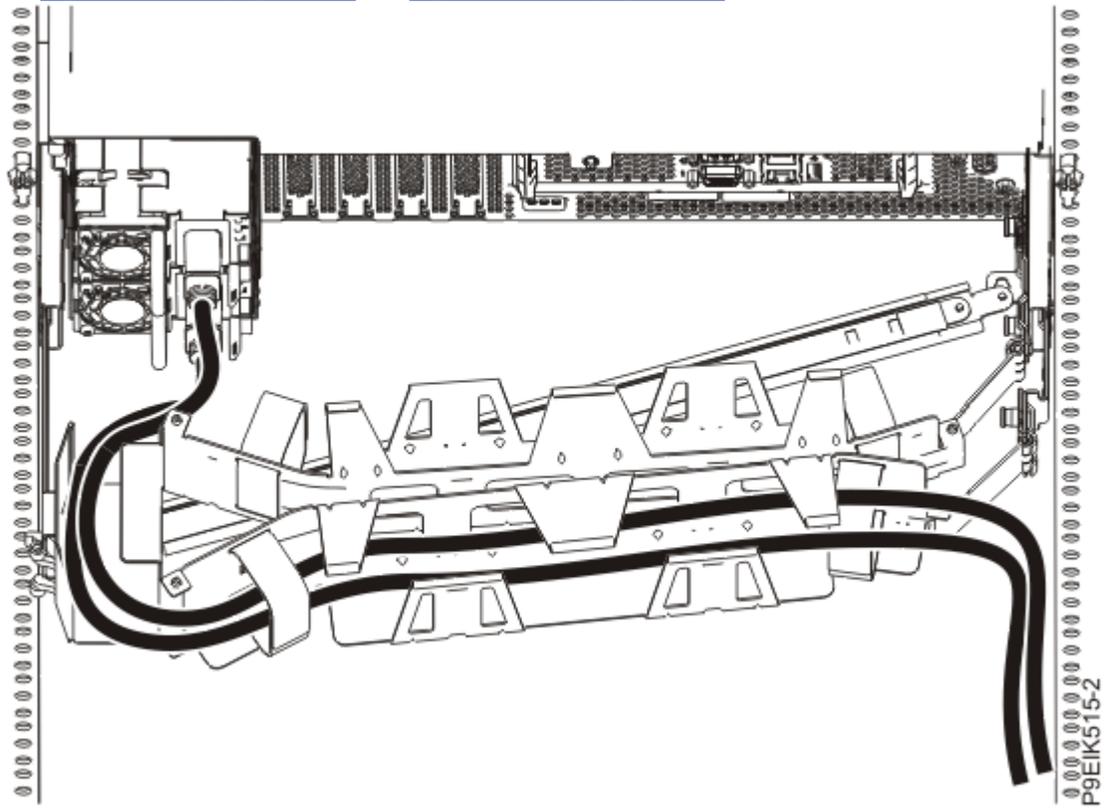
Enrollado del cable de alimentación en el brazo portacables
